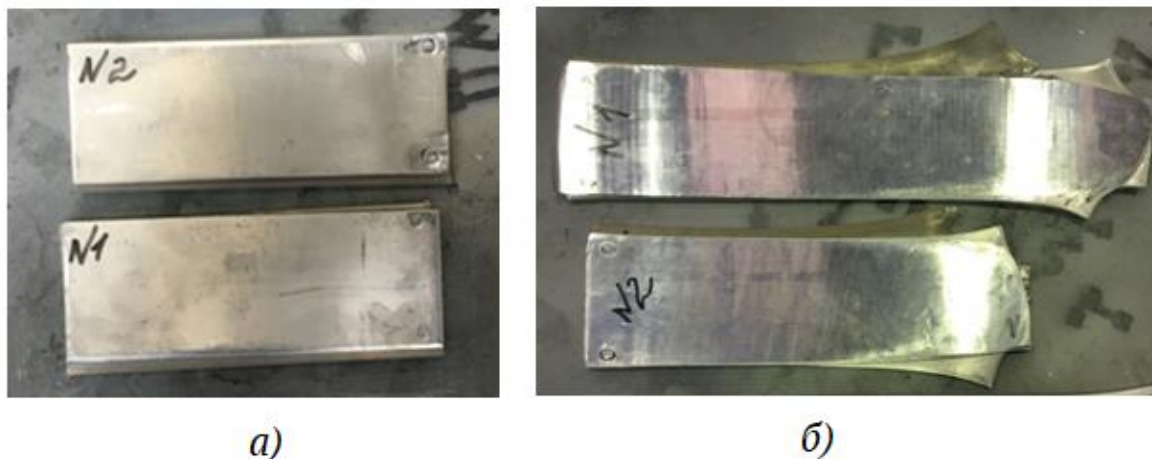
Заготовки-пакети до (а) та після (б) прокатки
